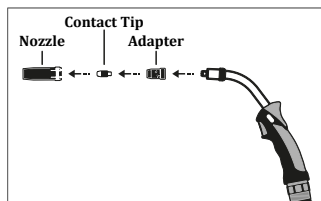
Retrait de la buse, du tube contact et de l'adaptateur
